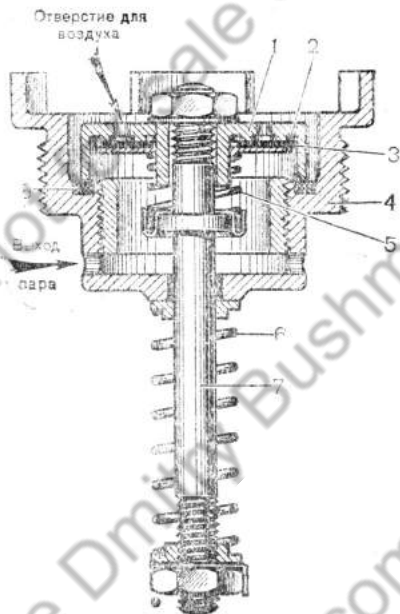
Паровоздушный клапан: 1 — паровой клапан; 2 — воздушный клапан; 3 — резиновые прокладки; 4 — корпус; 5, 6 — пружины; 7 — стержень
